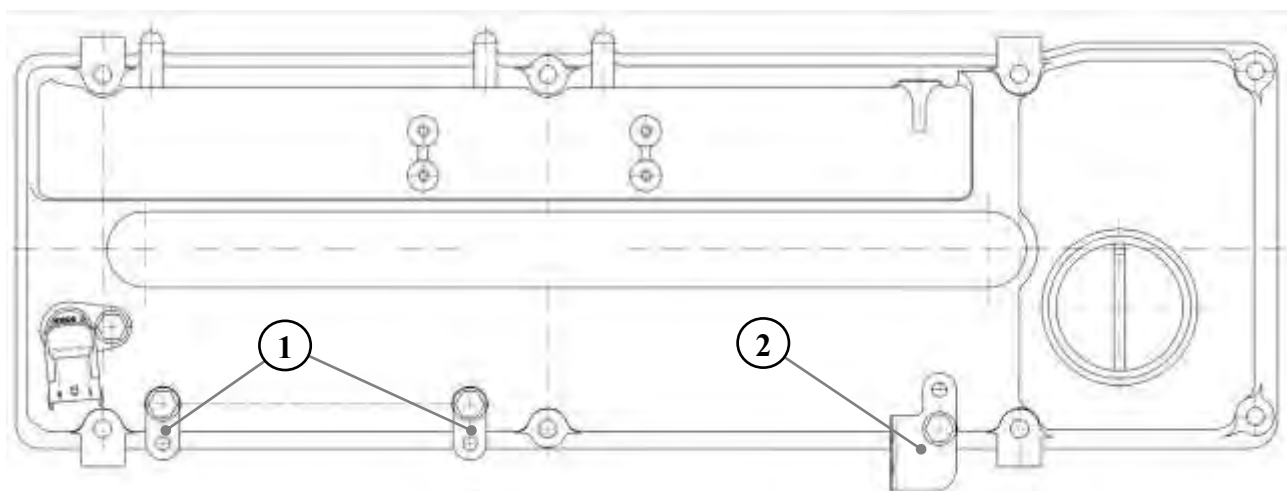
Схема установки скоб и держателей скоб крепления проводов:
